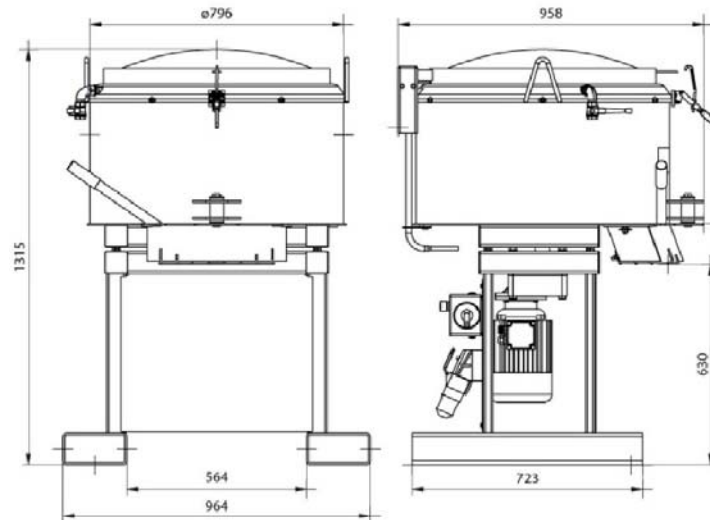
Esquema dimensional de la mezcladora DZ-120V.
